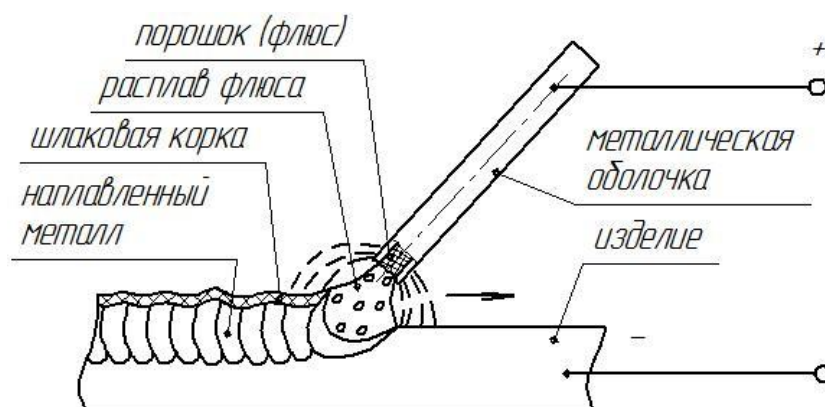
Схема выполнения наплавки порошковой проволокой
